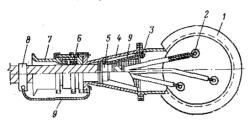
Общий вид сухой заделки кабеля вводного устройства: 1—вводная коробка; 2—проходные шпильки; 3—заземляющая шпилька; 4—воронка; 5— хомут для заземления свинцовой оболочки; 6— резиновое кольцо; 7— уплотияющий фланец; 8—хомут для заземления броии; 9— заземляющая перемычка
